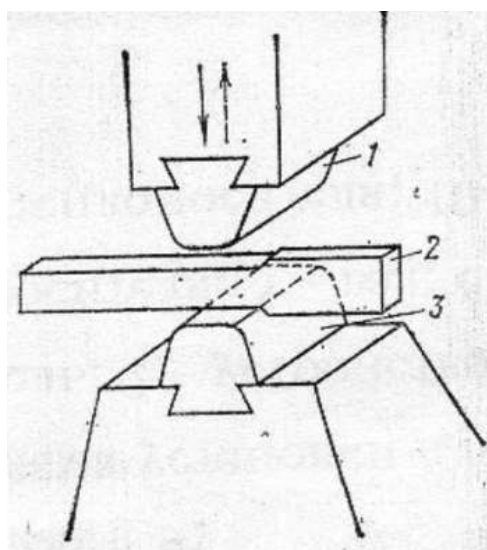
Схема процесса свободнойковки: 1 – верхний боек; 2 – заготовка; 3 – нижний боек
